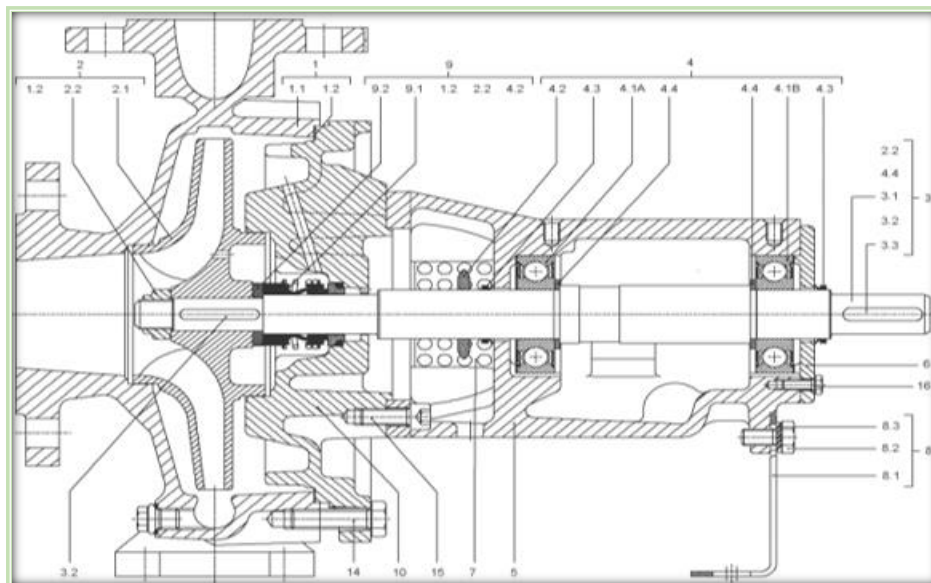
Dessin d'ensemble de pompe centrifuge WILO
